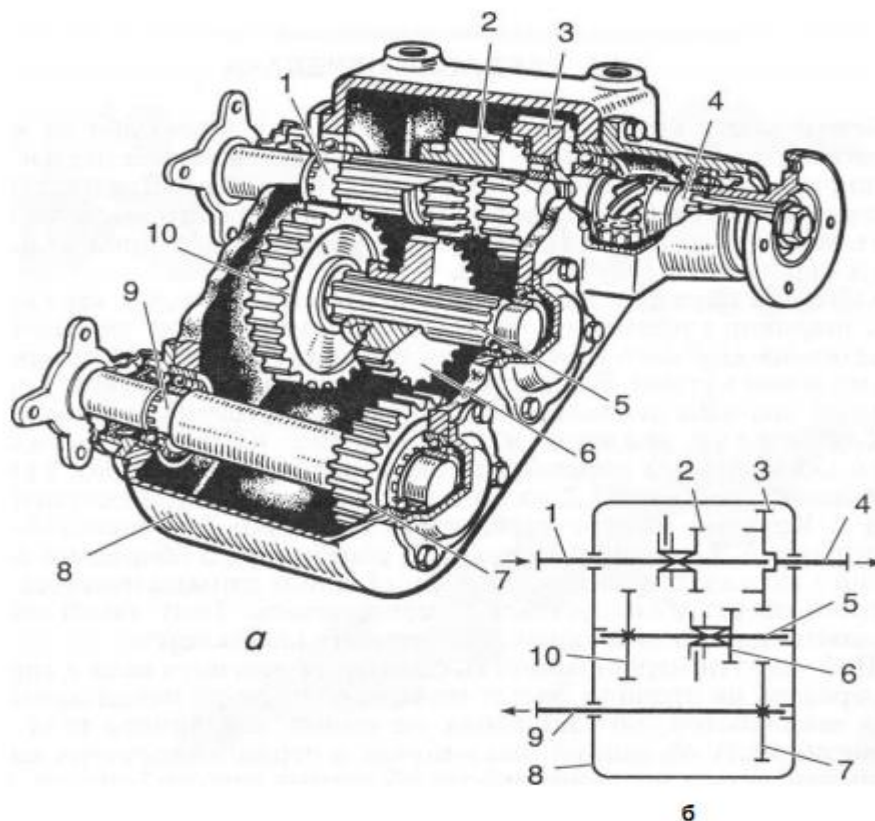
Роздавальна коробка з прямою та знижувальною передачами : а — загальний вигляд; б — кінематична схема; 1 — ведучий вал; 2, 3, 6, 7, 10 — шестерні; 4 — ведений вал; 5 — проміжний вал; 8 — корпус; 9 — вал привода переднього моста.
